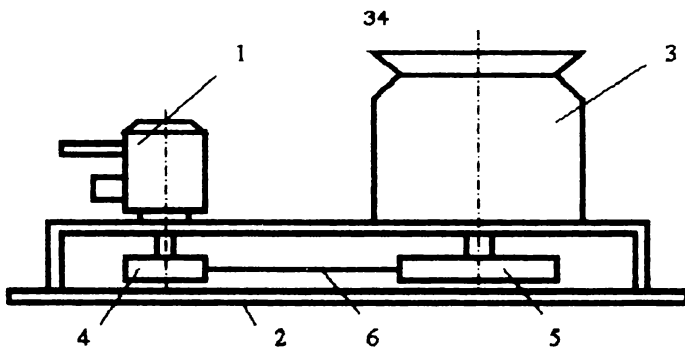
Общий вид измельчителя корнеслубяеплодов.
